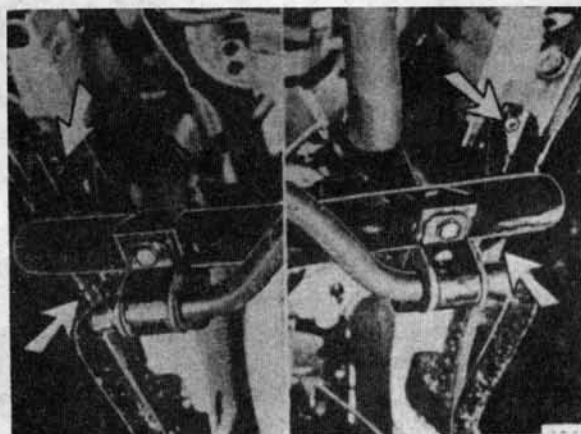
Расположение болтов крепления двигателя B172 к передней поперечной балке
